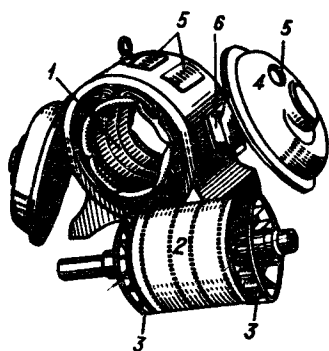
Разобранный асинхронный двигатель с короткозамкнутым ротором
